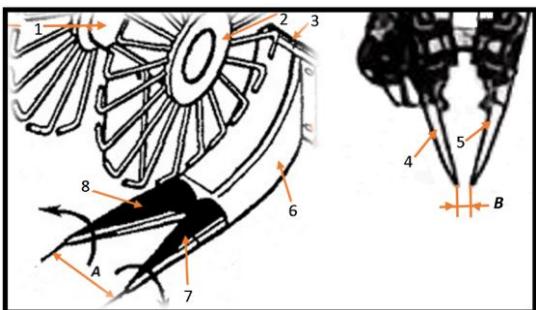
Схемное изображение выкапывающего устройства свеклоуборочного комбайна РКС-6: 1 – корнезаборник правый; 2 - корнезаборник левый; 3 – прокладки регулировочные; 4 – корнезаборник правый; 5 – корнезаборник левый; 6 стойка; 7 – активная вилка левая; 8 – активная вилка правая; А – расстояние между вилками; В - расстояние между корнезаборниками.
